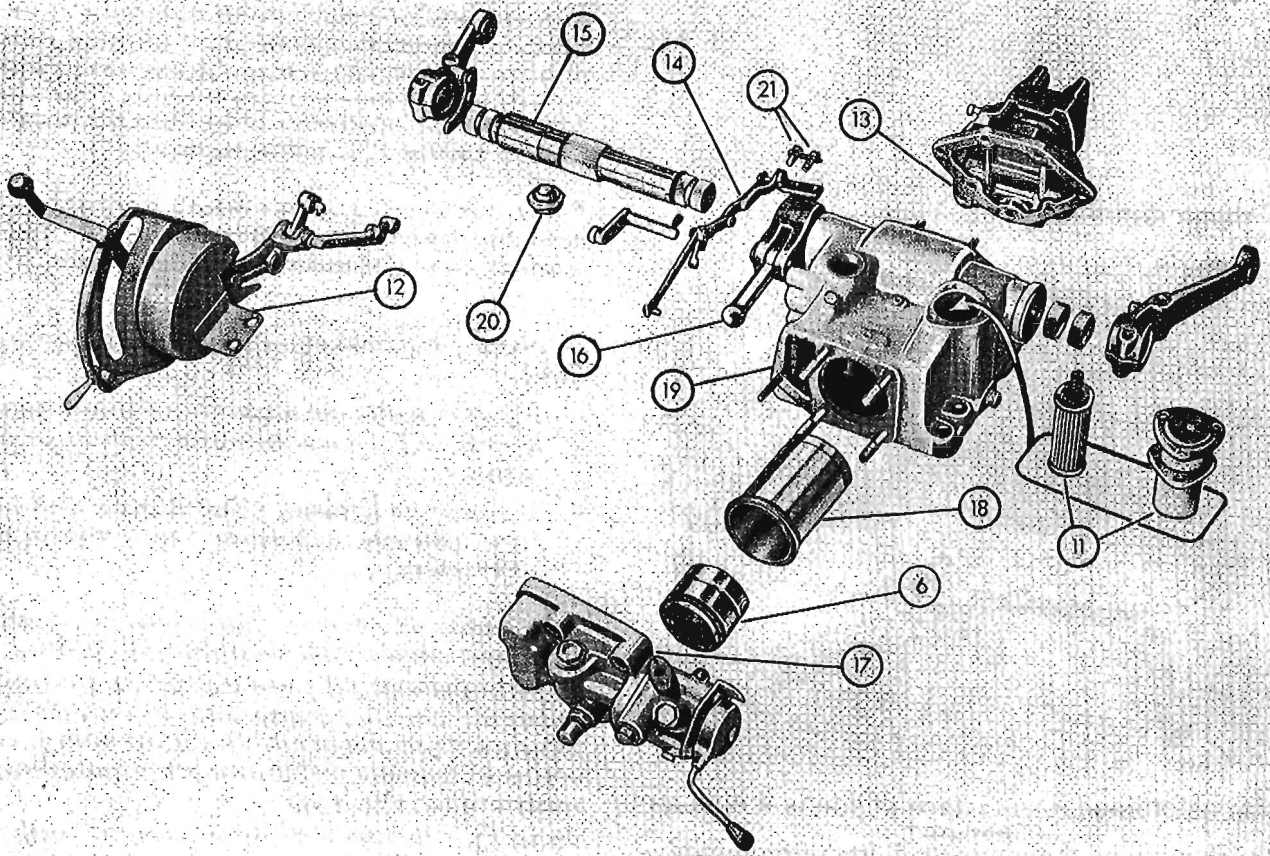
Gruppi smontati dal sollevatore idraulico.
